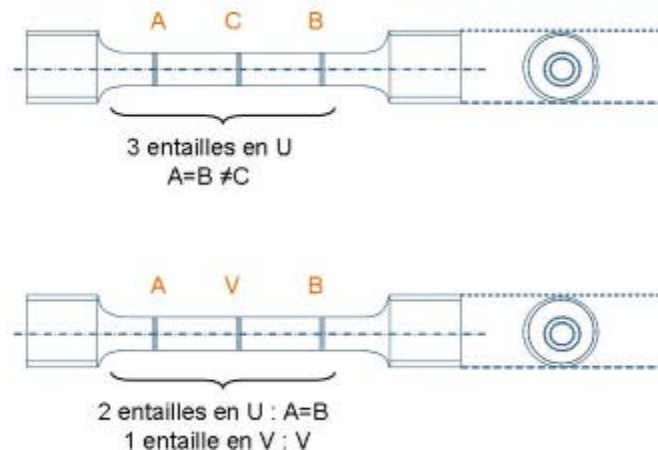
Emplacement des entailles sur le fût de l'éprouvette, 3 éprouvettes entaillées et 1 éprouvette lisse
